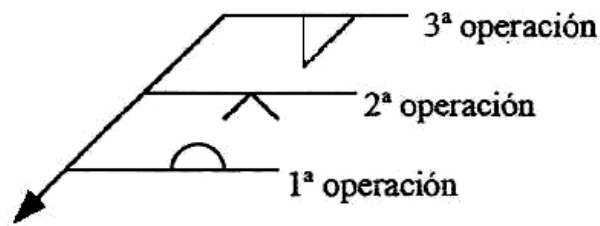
SÍMBOLO DE SOLDAR CON LÍNEAS DE REFERENCIA MÚLTIPLES.
